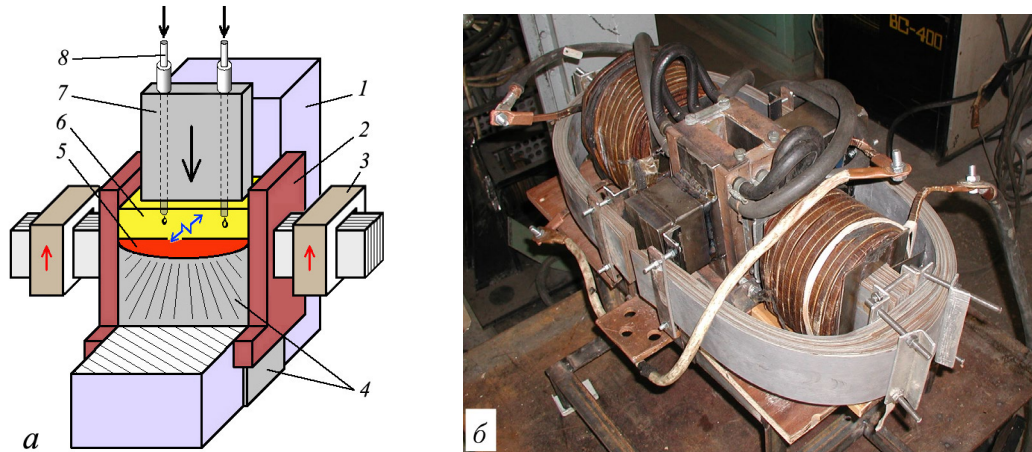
Схема електрошлакового зварювання плавким мундштуком в поперечному магнітному полі (а) і зовнішній вигляд електромагнітного пристрою (б): 1 – плита, яку зварюють; 2 – формуючі планки; 3 – електромагнітний пристрій; 4 – зварний шов; 5 – металева ванна; 6 – шлакова ванна; 7 – плавкий мундштук; 8 – електродний дріт
